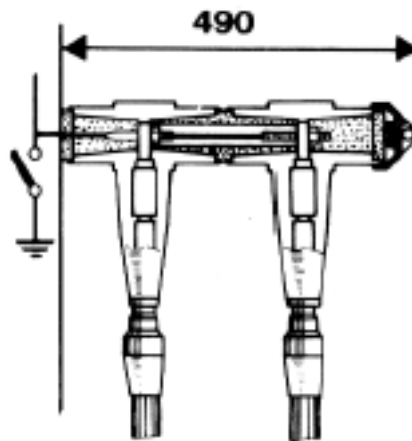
Accesorio de unión de terminales enchufables en paralelo para de 20 kV.
